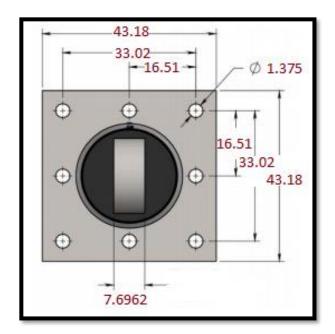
Dimensiones de la placa base del disipador de 330kip. Fuente: Propia
